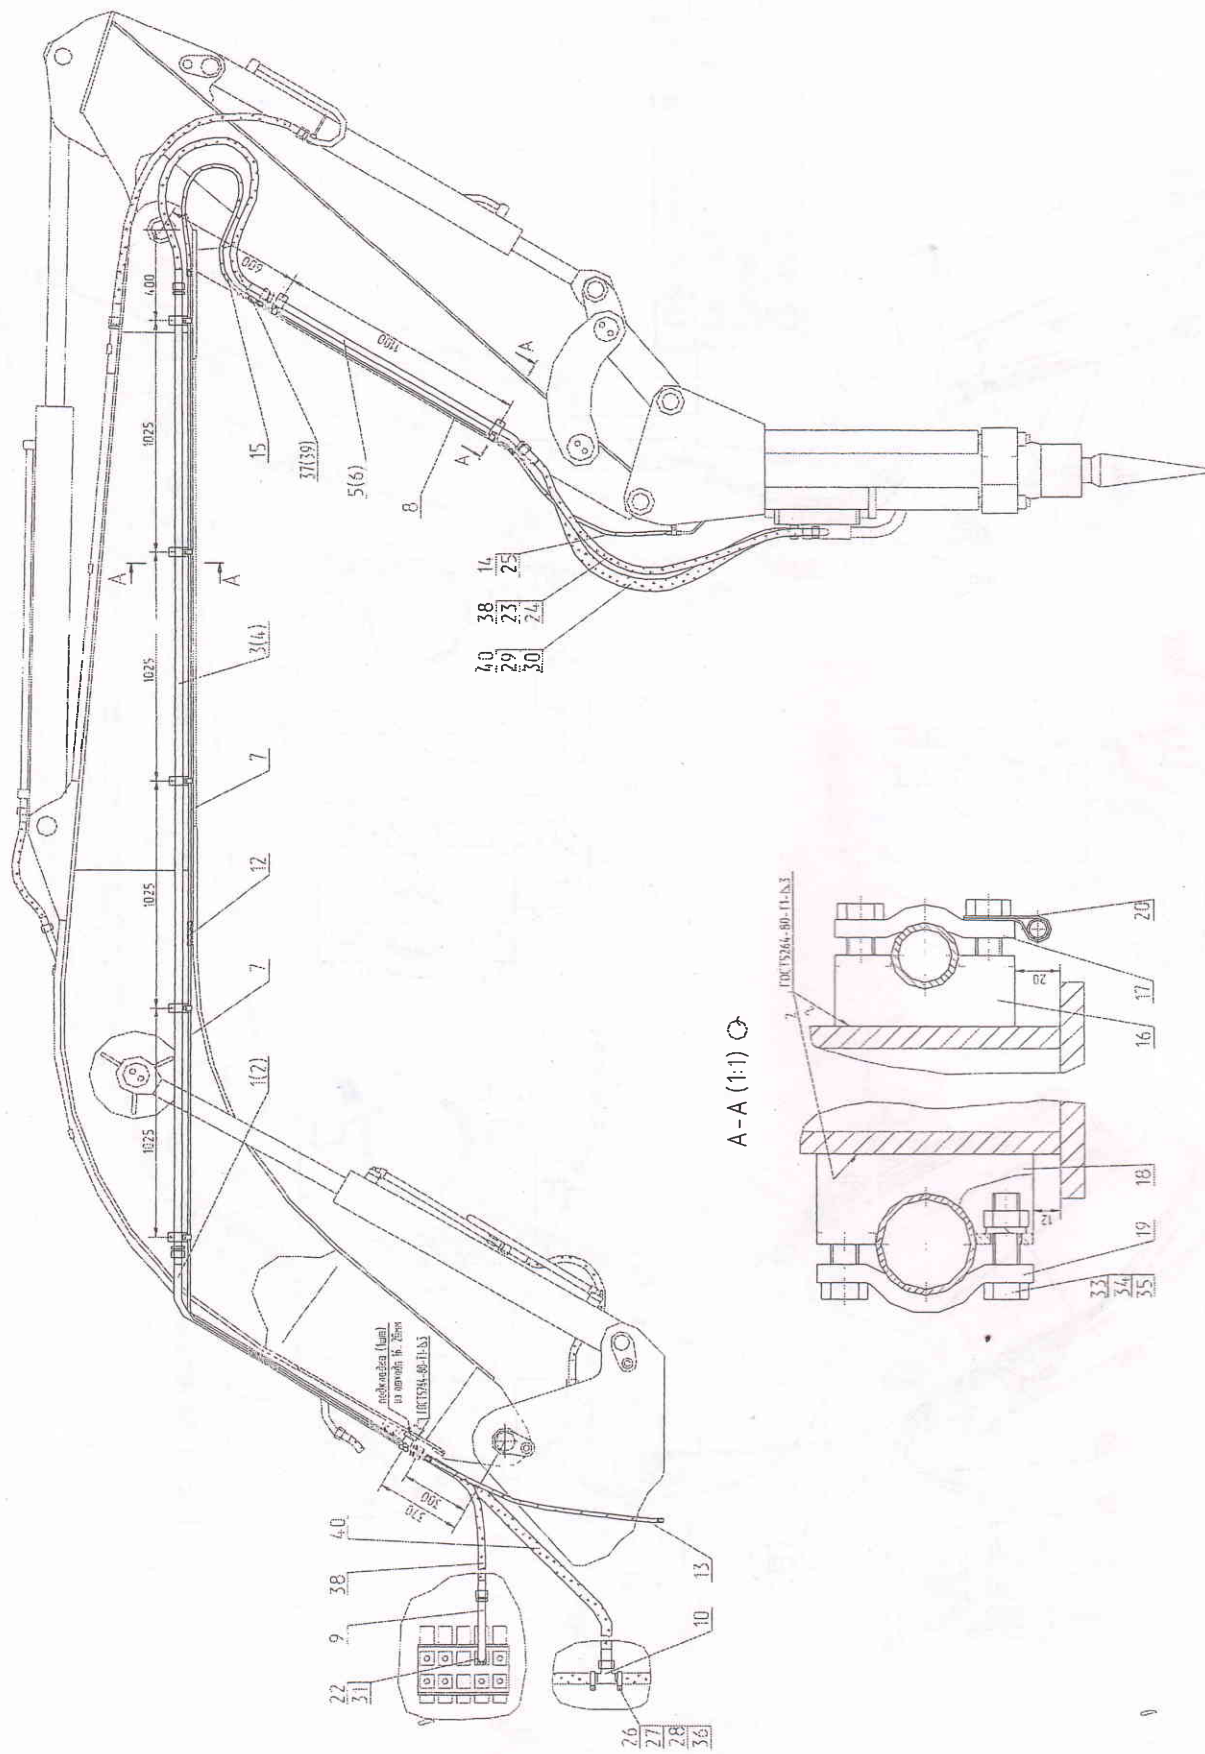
Монтаж гидрооборудования гидромолота на рабочем оборудовании экскаватора ET-25
